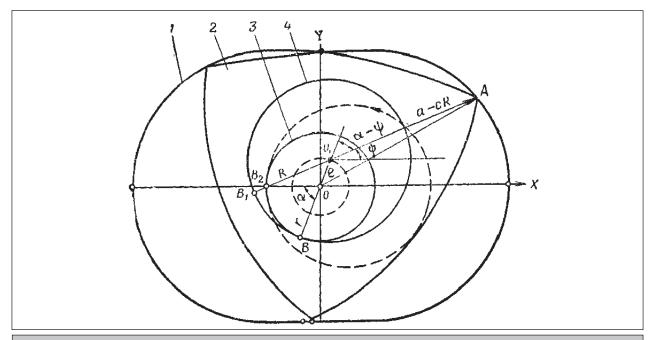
Кинематическая схема роторного двигателя: 1 — корпус двигателя; 2 — ротор; 3 — неподвижная синхронизирующая шестерня с радиусом r; 4 — подвижная синхронизирующая шестерня с радиусом R; α — угол поворота эксцентрикового вала; ϕ — угол поворота ротора; a-cR — производящий радиус; c — параметр формы; O — неподвижный центр вращения эксцентрикового вала; O_1 — подвижный центр вращения ротора
